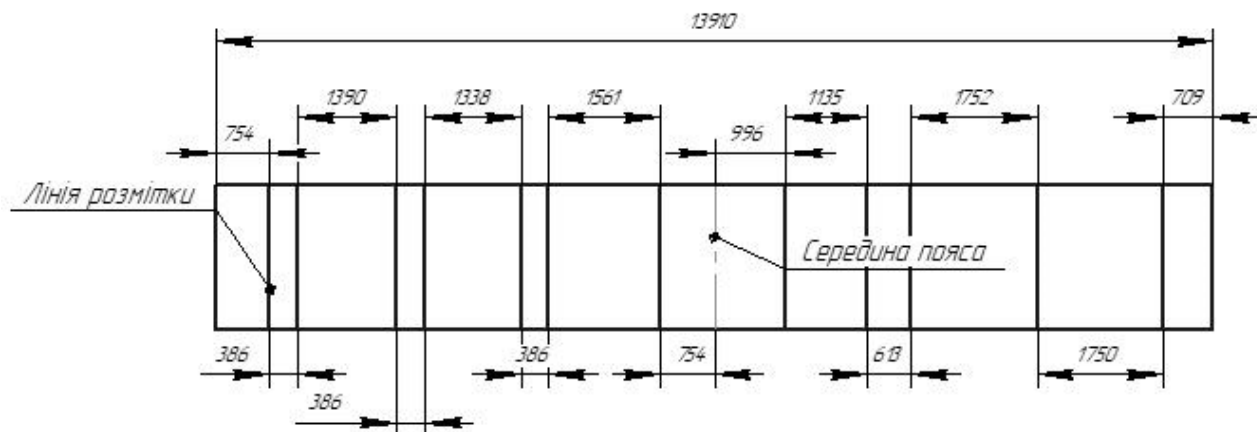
Схема розмітки верхнього пояса для установки діафрагм
